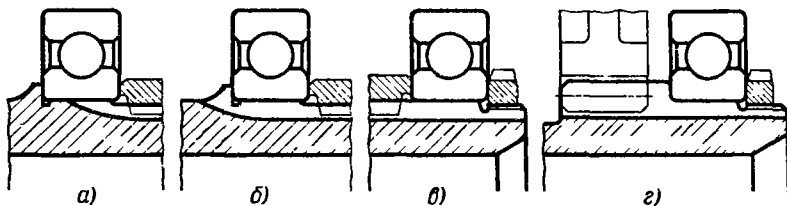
Установка подшипников на неполных цилиндрических поверхностях
